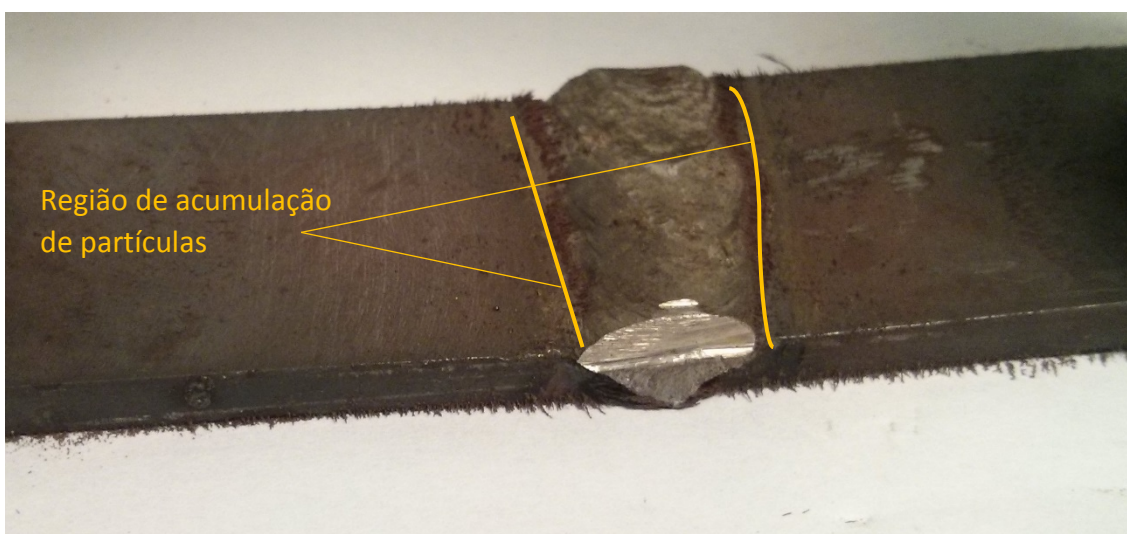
Defeitos presentes na zona adjacente ao cordão de soldadura da amostra 18_POP300WP700 observados nos ensaios de partículas magnéticas
